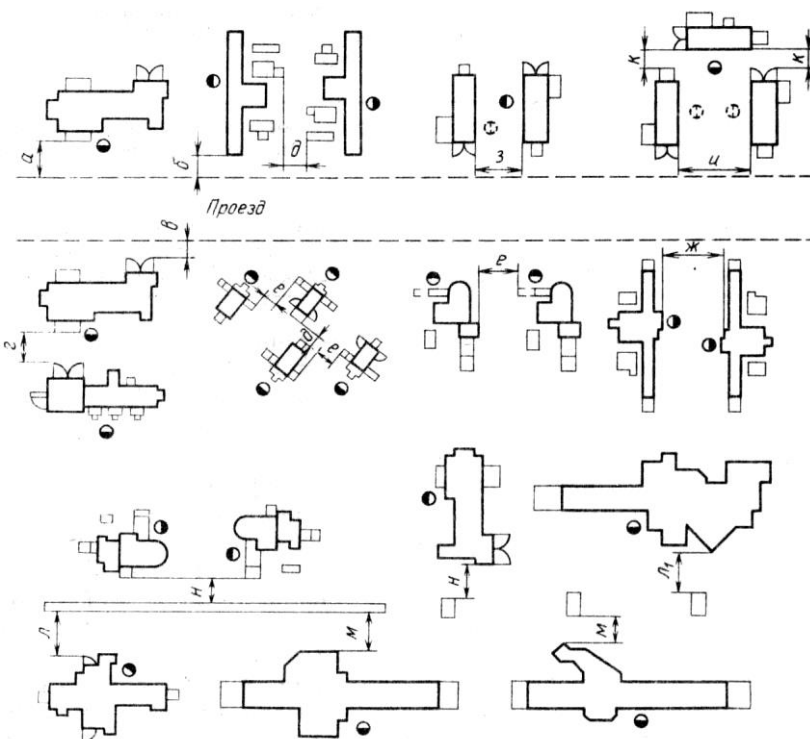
Размещение станков с учетом расстояний от проезда, относительно друг друга, от стен и колонн здания
